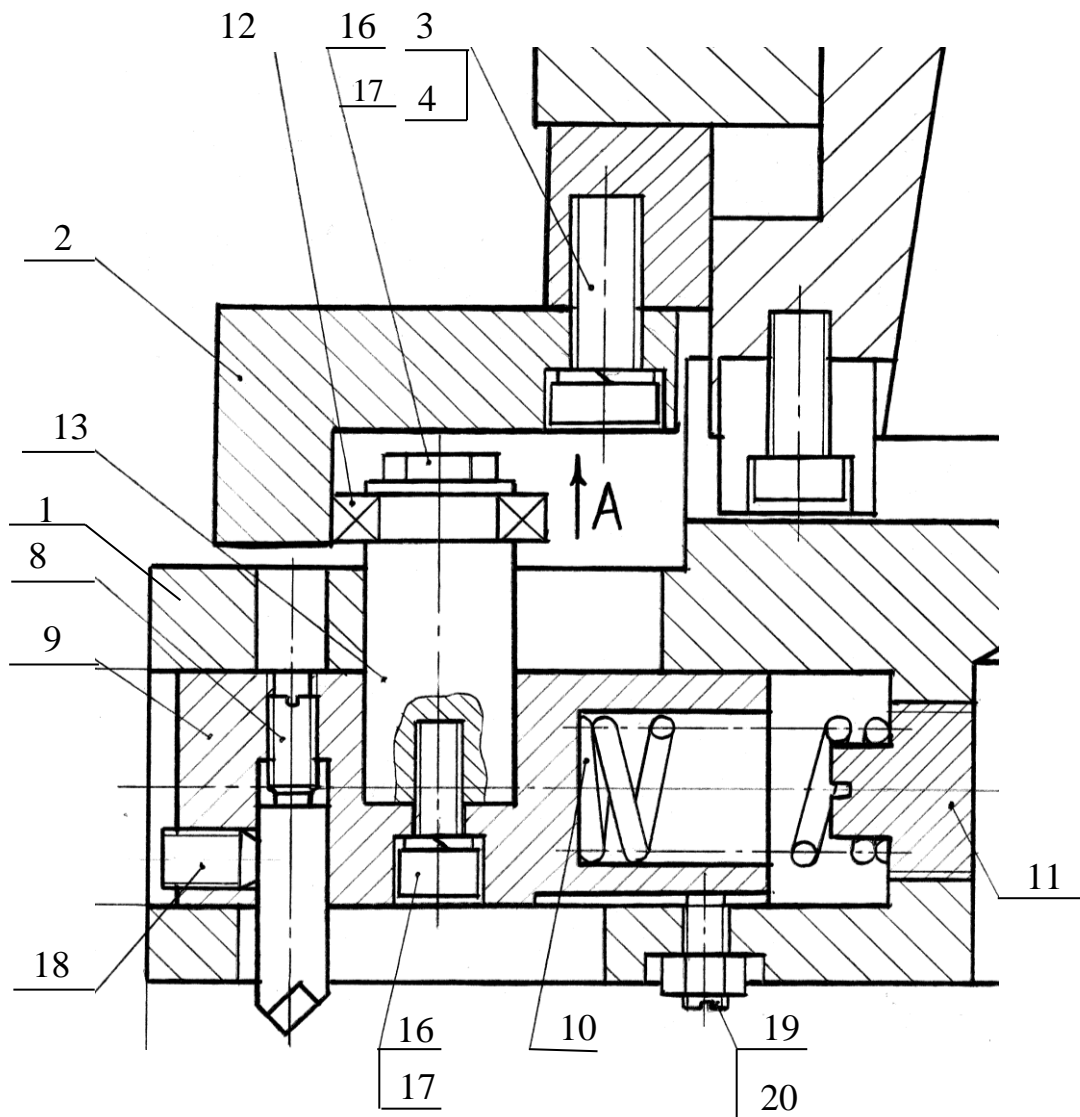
Конструкція торцевої фрези з комбінованою схемою різання
